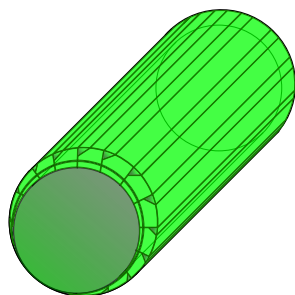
Braçadeira Plástica com Dobras – A aplicação da técnica de dobra permite que a braçadeira esteja folgada, para quando insuflada, a sua geometria crescer para o exterior
